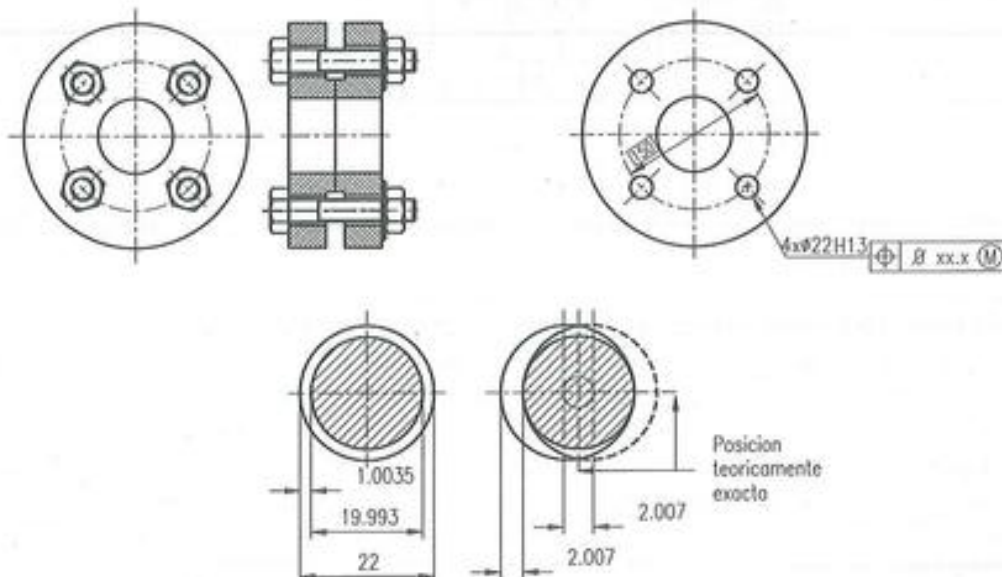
Diseño de un acoplamiento atornillado con agujeros pasantes en las dos bridas.
